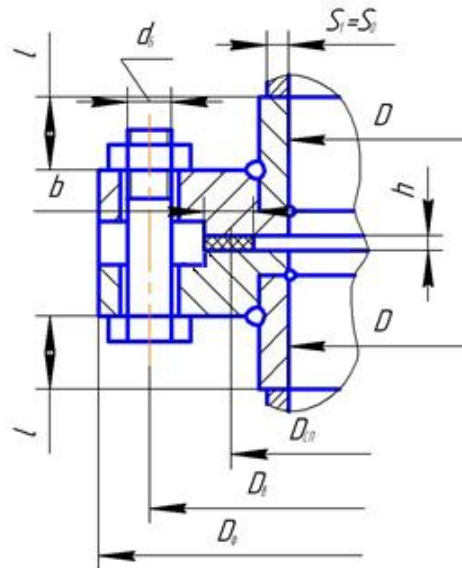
Розрахункова схема фланцевого з'єднання
